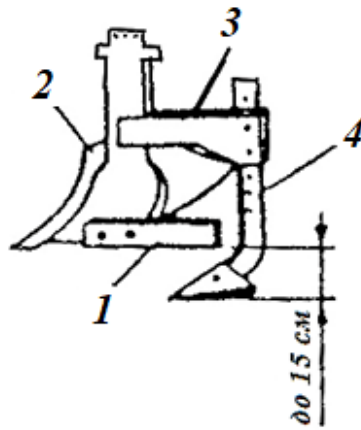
Змінний корпус з ґрунтопоглиблювачем:
